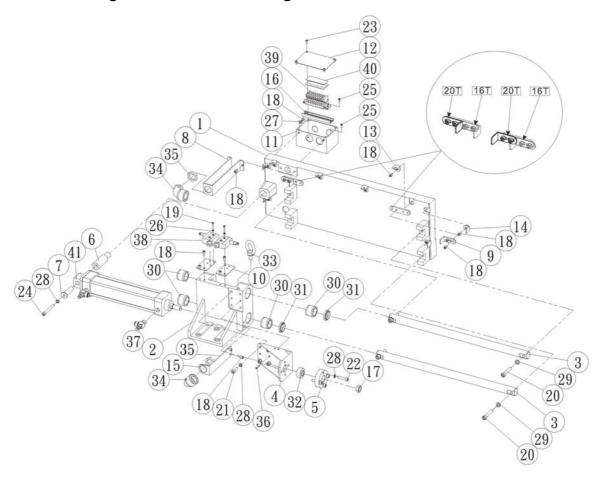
Werkzeugwechsler 2-4 -Tool changer 2-4
